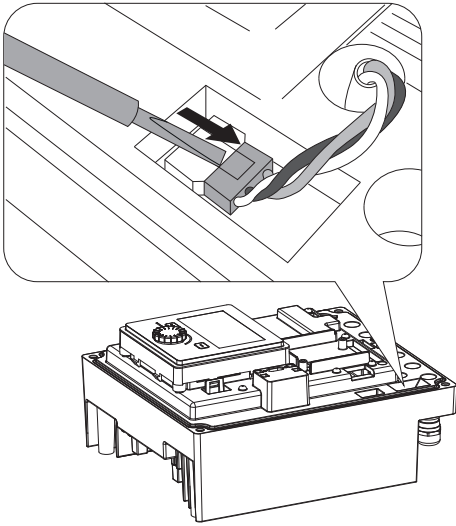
Soltar el cable de conexión del ventilador del módulo
